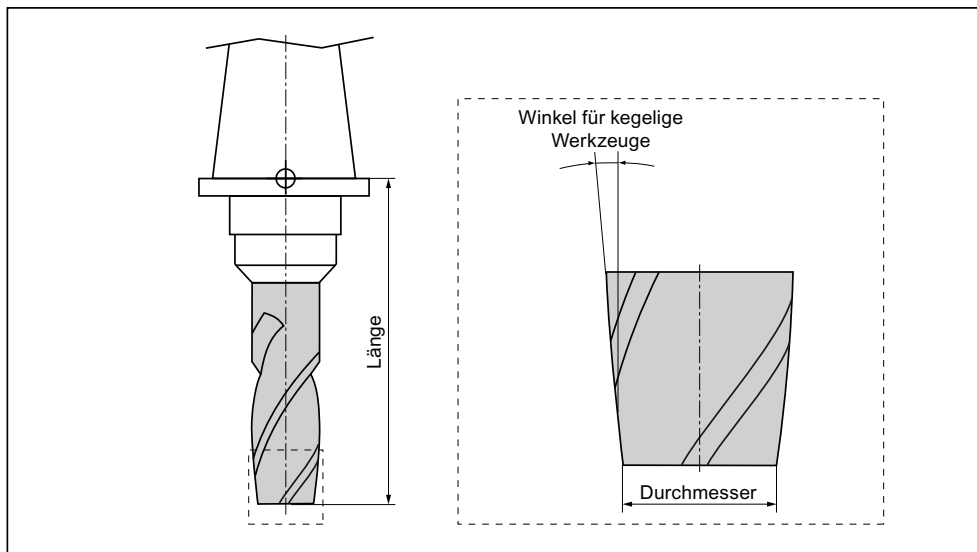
3D-Werkzeugtyp am Beispiel eines Kegelstumpffräasers (Typ 155)
